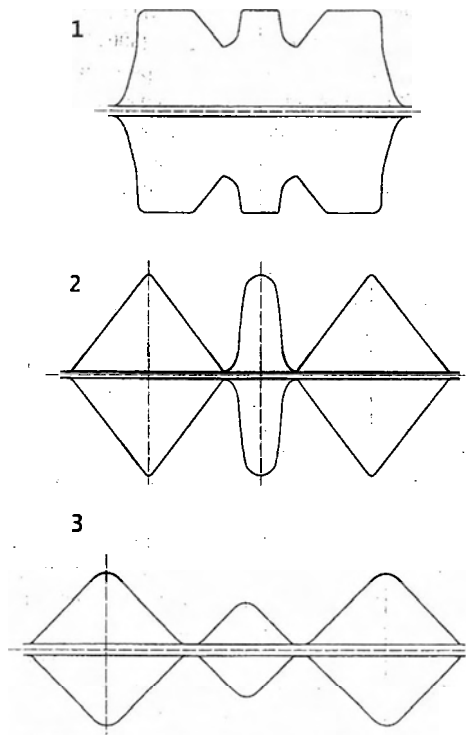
Форма калибров валков клетки 900 для многоручьевой прокатки-разделения раскатов с удалением ликвационной зоны: 1 - центрирующий; 2 - формирующий; 3 - разделяющий калибры.
